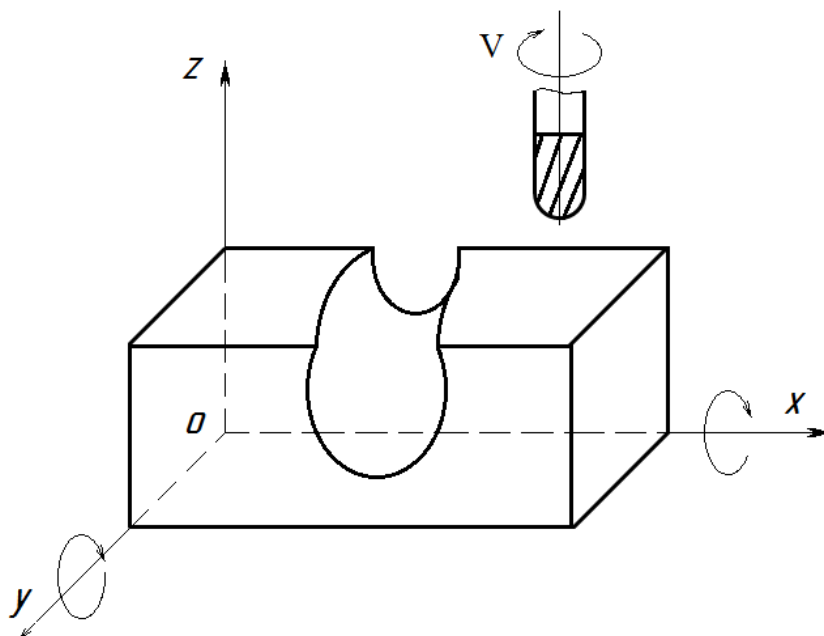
Схема движений пятикоординатного фрезерного станка
